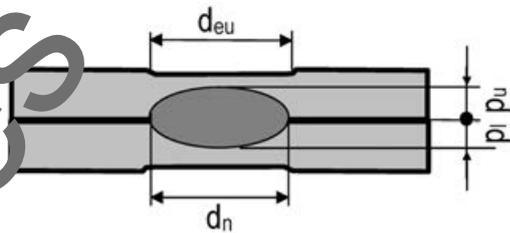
Größen zum Erfassen von Form und Ausdehnung einer Punktschweißverbindung bei gleicher Blechdicke (einschnittig).
